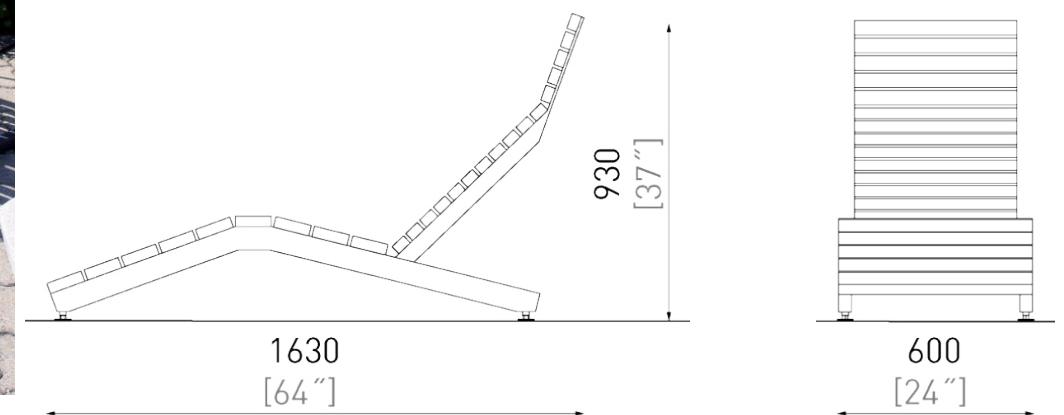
Technický detail - lavička Preva Urbana (zdroj: www.mmcite.com)
